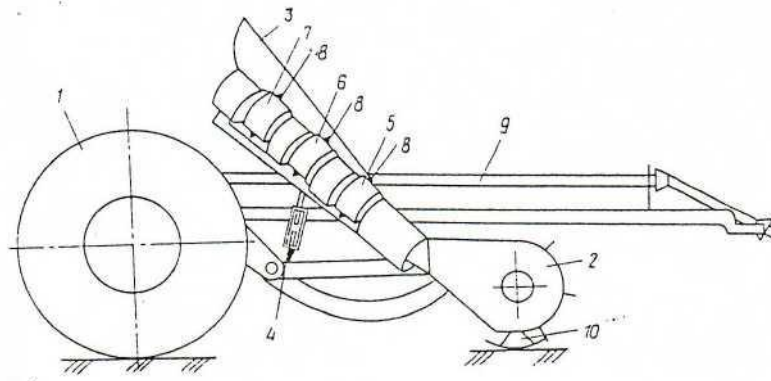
Пристрій для обертання валків [17], вид збоку
